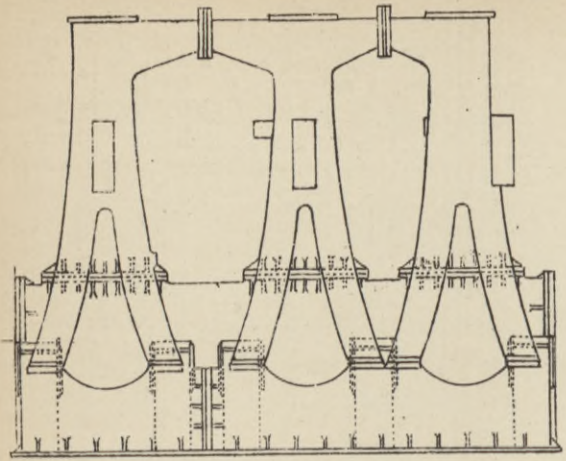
Grundplatte und Frame einer Dreifach-Expansionsmaschine.
